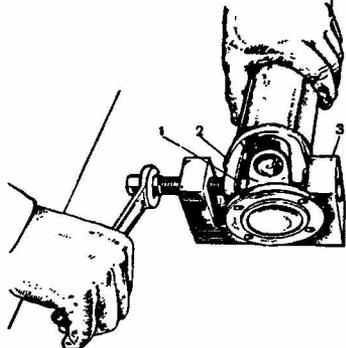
Выпрессовка подшипников крестовины из вилок карданного шарнира: 1 - игольчатый подшипник; 2 - вилка карданного шарнира; 3 - струбцина 67.7823.9522
